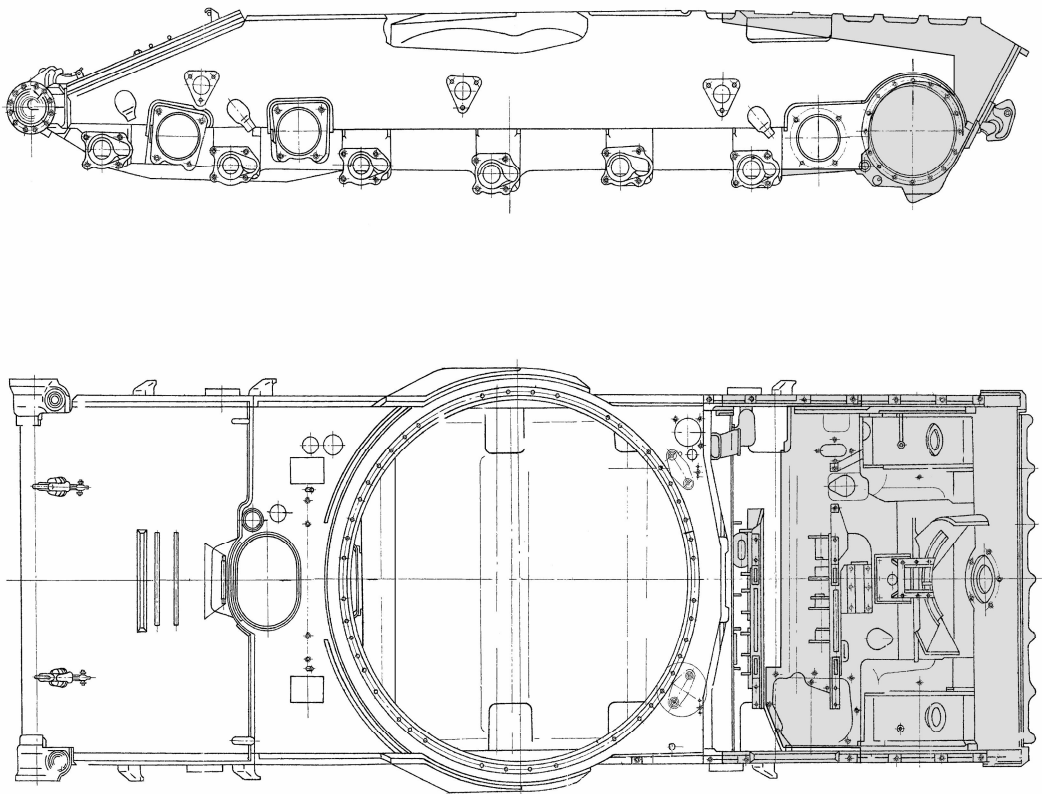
Схема порезки кормы корпуса танка Т-72 под установку двигателя 5ТДФМА
